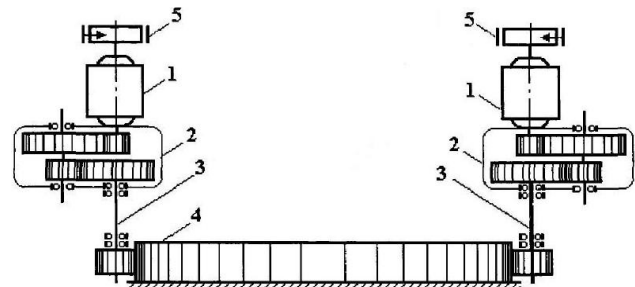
Кинематическая схема механизма поворота экскаватора
